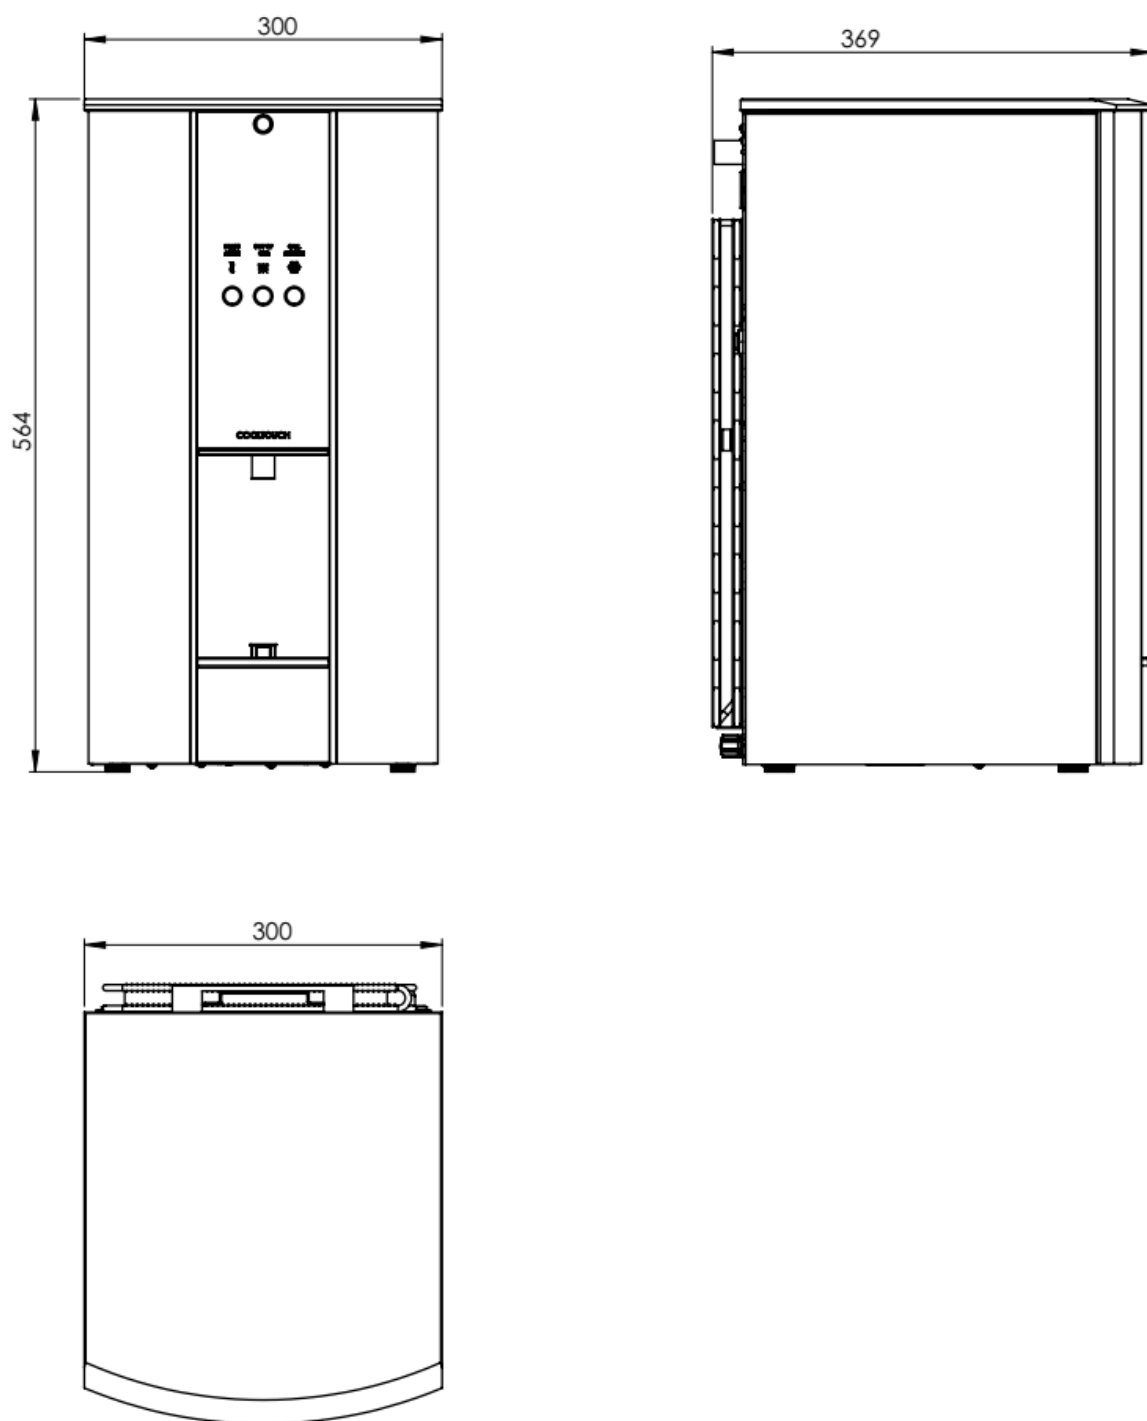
Габаритные размеры модели СТР-03*-CHS-S-V20-2С
